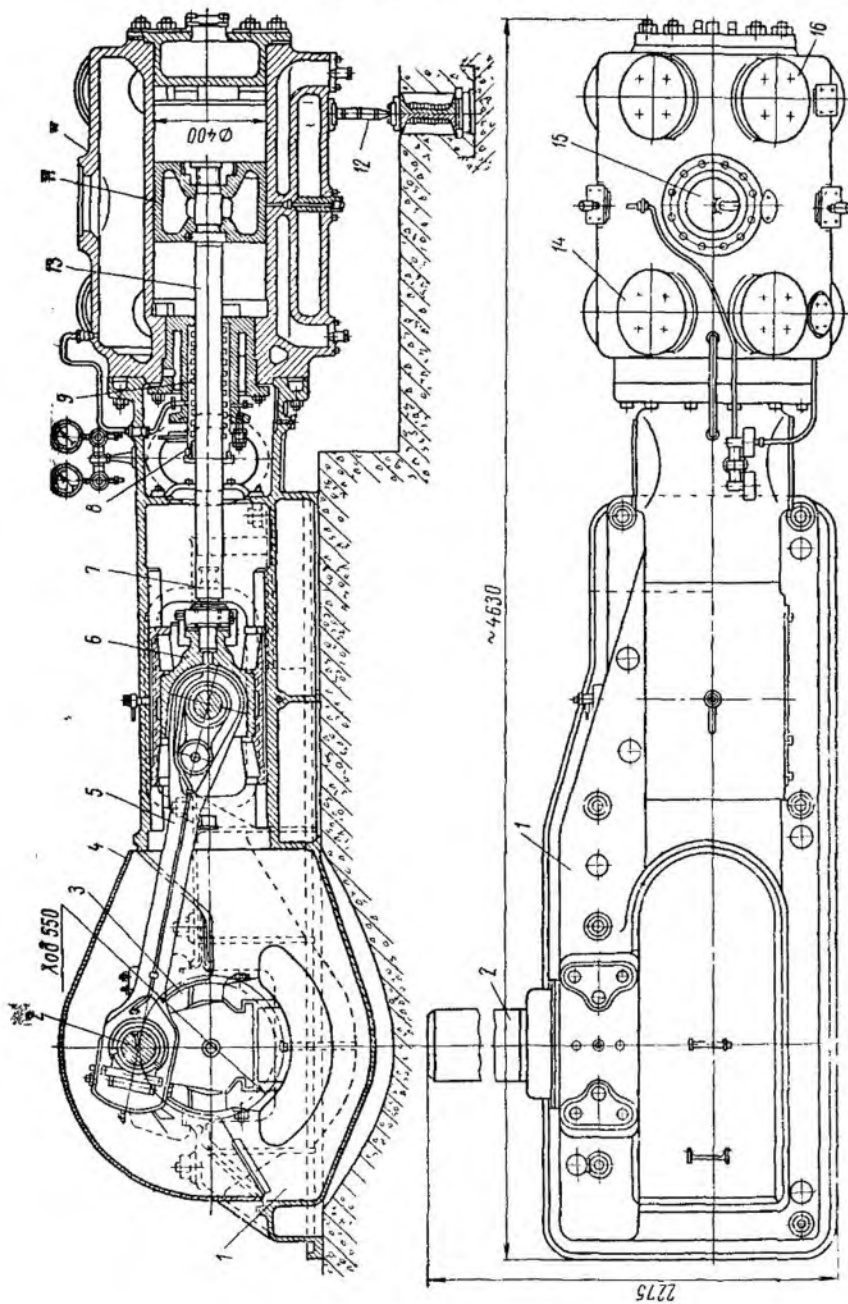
Горизонтальный аммиачный компрессор двойного действия АГ-600:
